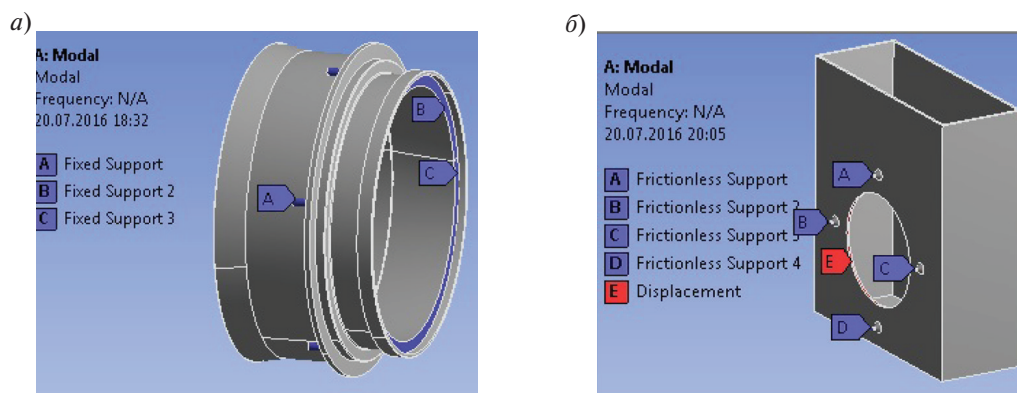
Расчетные схемы закрепления выходной конусной части (а) и корпуса патрубка (б)
